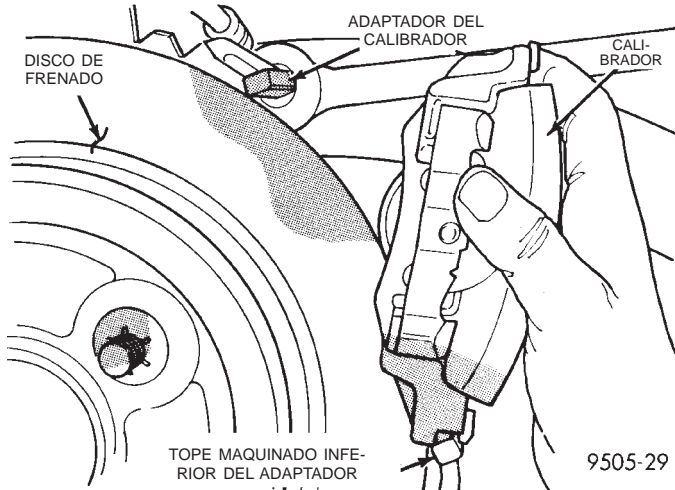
Desmontaje/Instalación del conjunto de calibrador del adaptador
